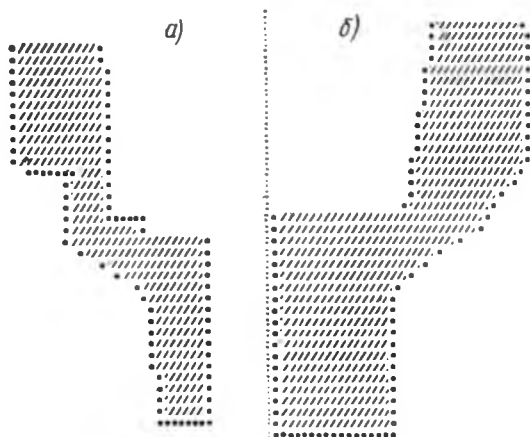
Эскизы детали (а) и поковки (б), полученные на АЦПУ ЭВМ
